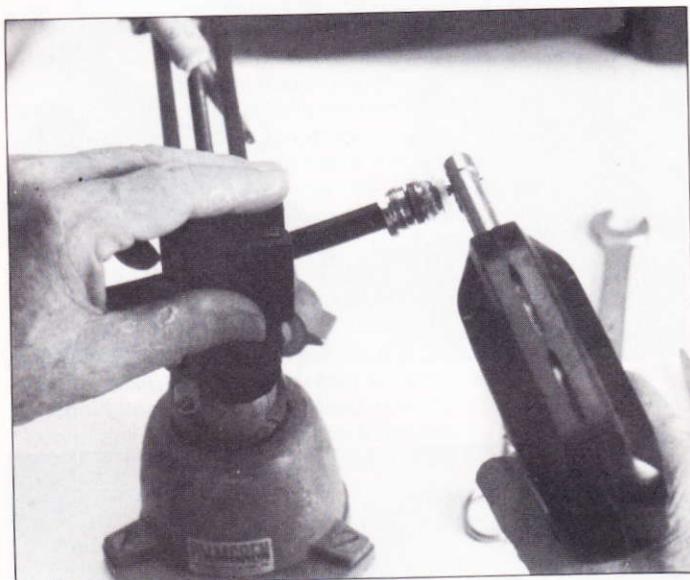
Aplicar y soldar la aguja del contacto central. Servirse del soldador de pistola sin la punta de cobre.
